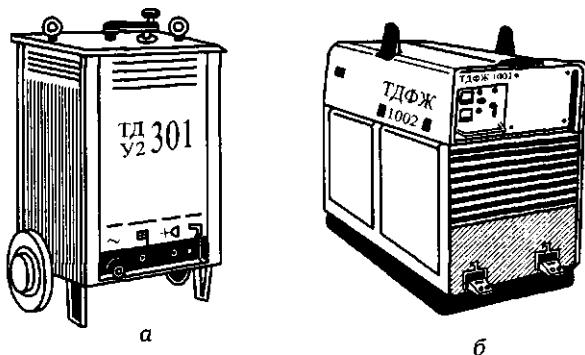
Сварочные трансформаторы серии ТД для ручной дуговой сварки (а) и серии ТДФЖ для сварки под флюсом (б)
